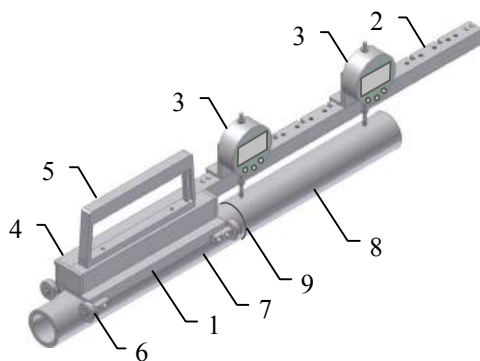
Конструкция измерительного блока: 1 – основание; 2 – штанга; 3 – индикаторы; 4 – корпус; 5 – ручка; 6 – подшипники; 7 – тело трубы; 8 – приваренный замок; 9 – сварной шов
